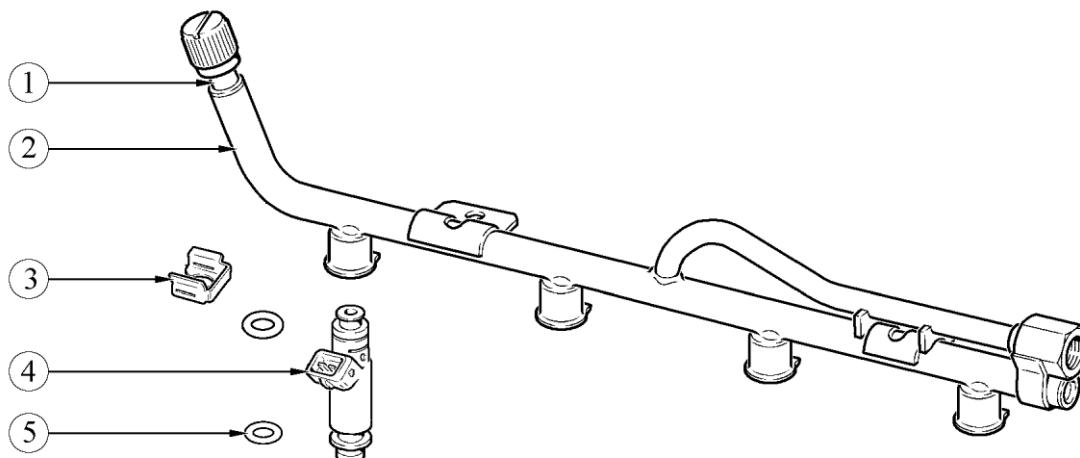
Рампа форсунок в сборе двигателя 21126:
